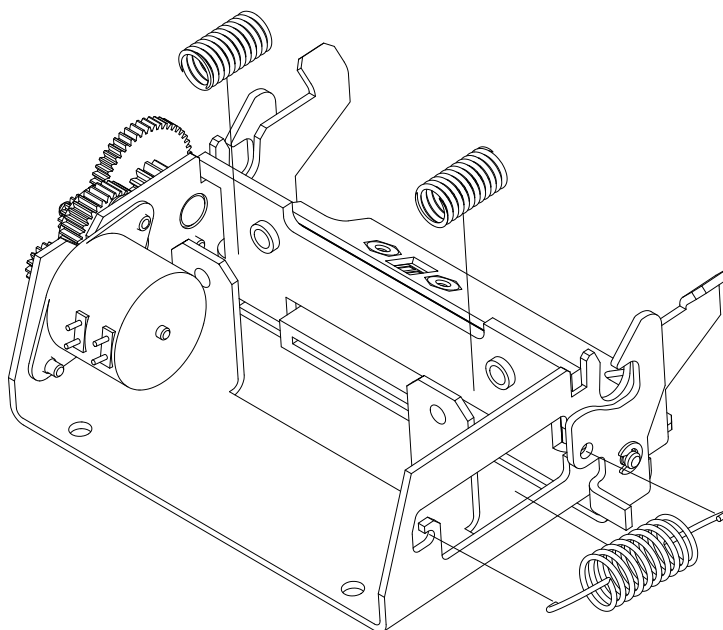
Пружины защелки прижимного вала чековой ленты и печатающей головки.
